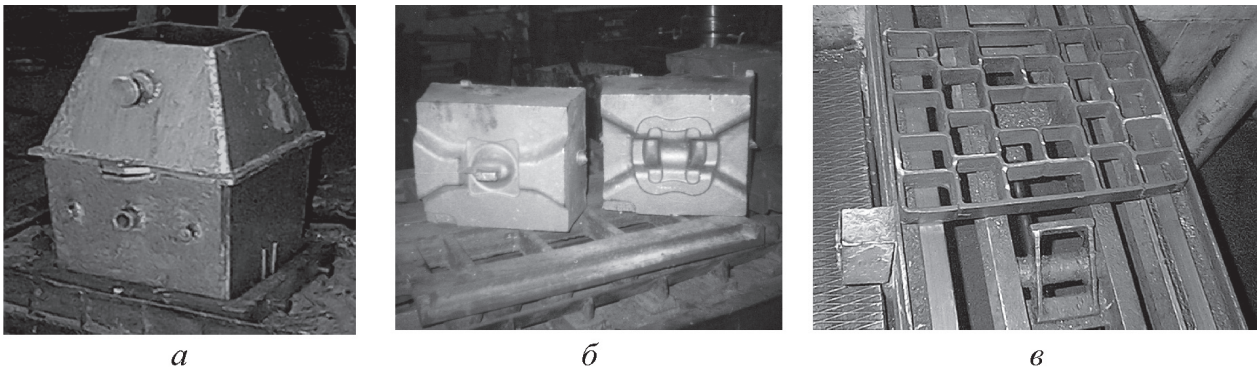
Металлооболочковая литейная форма (а), отливки вставок штампов (б), поддон для термических агрегатов из новой жаростойкой стали (в)
